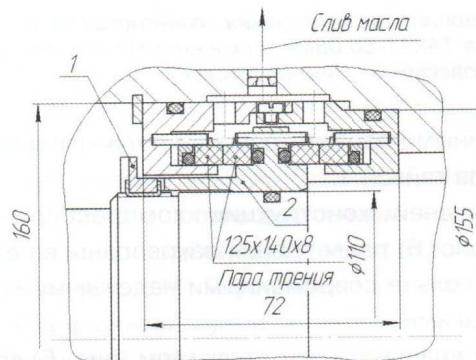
Двухстороннее уплотнение «пакетного» типа 6 базы компрессора 6ГВ-18/16 со свободно установленными парами трения (ГПП, г. Туймазы, респ. Башкортостан):
